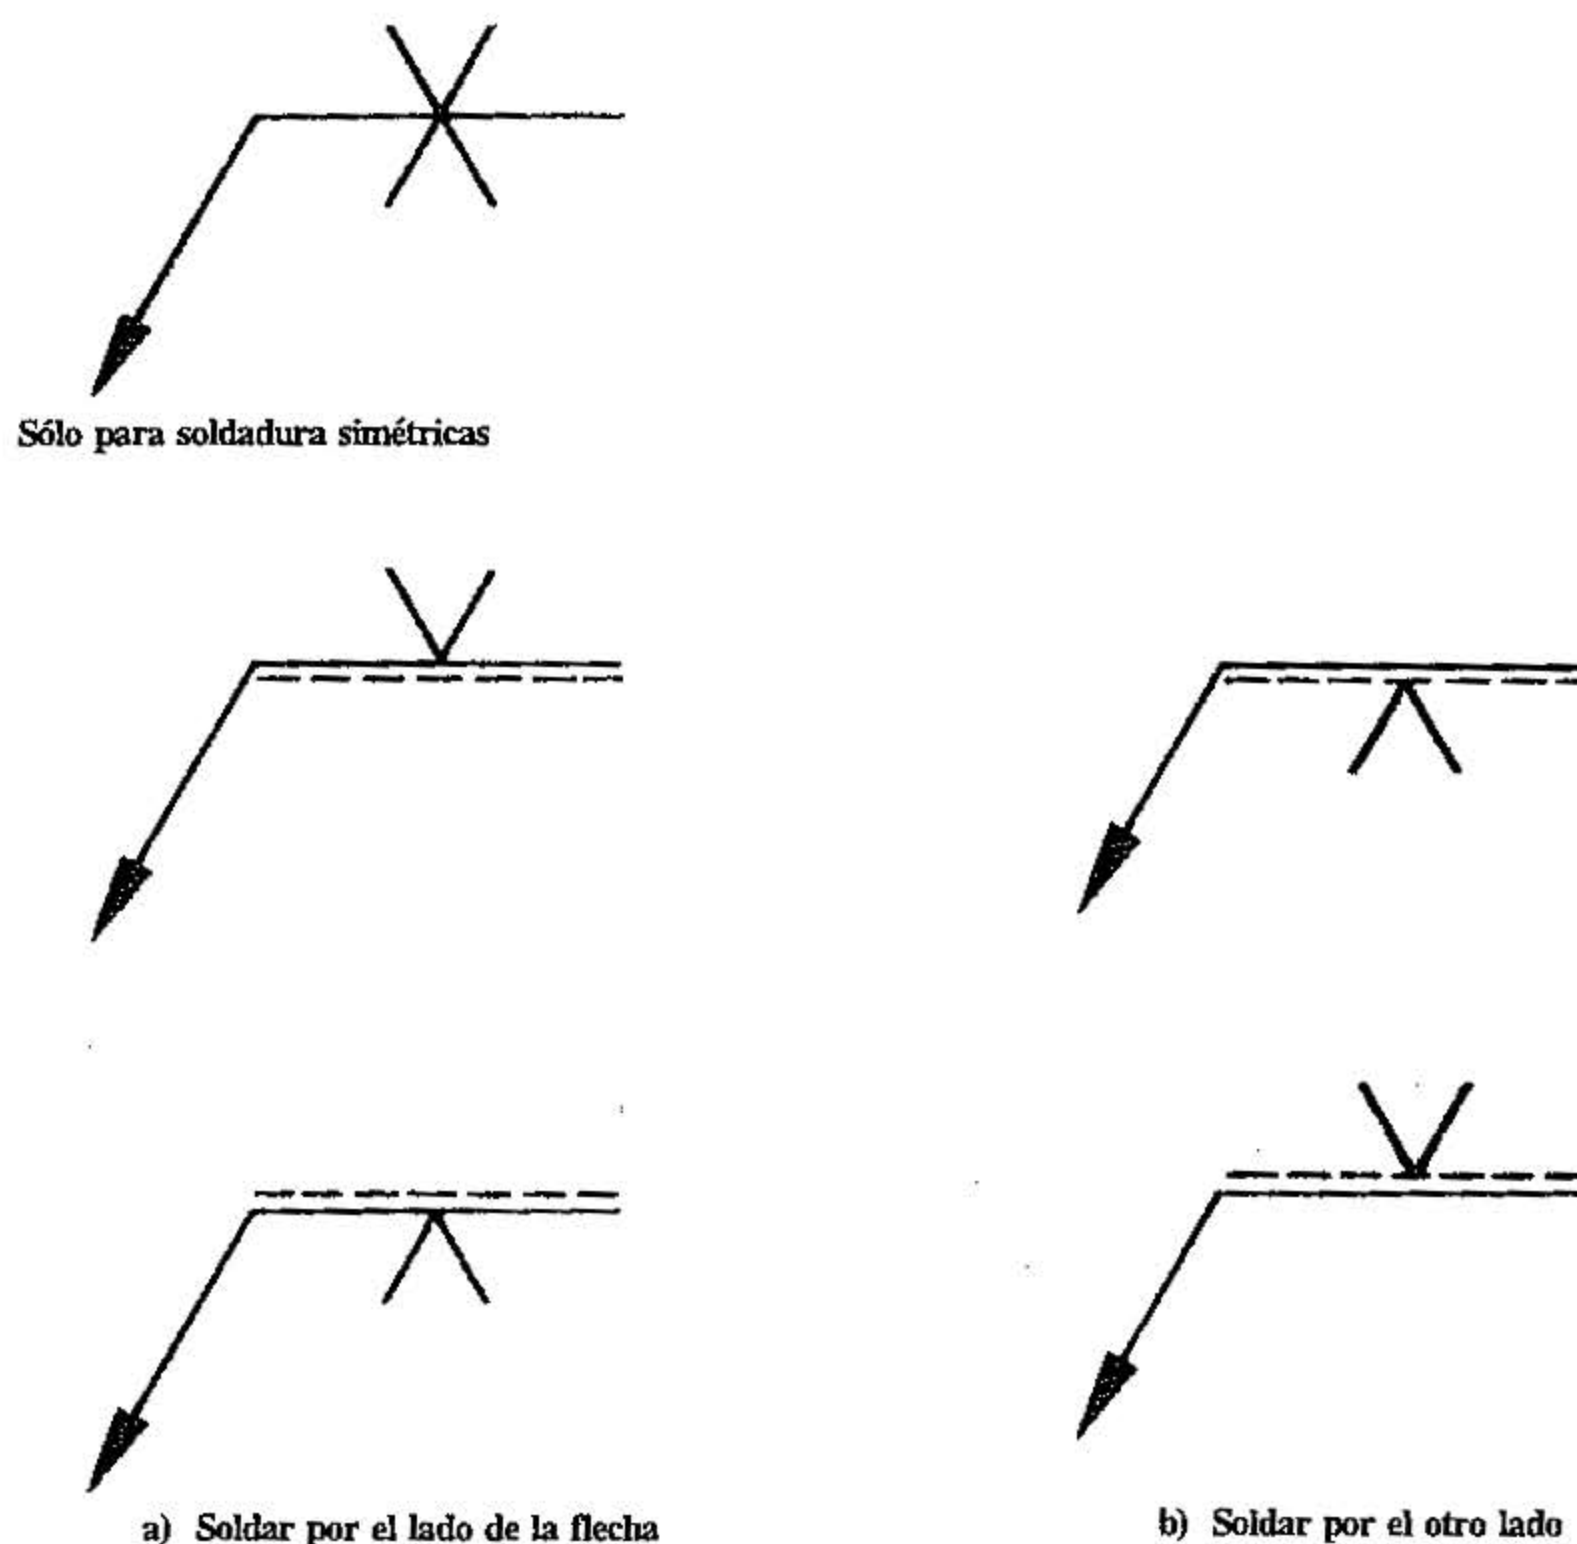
Posición de los símbolos de acuerdo con la línea de referencia
